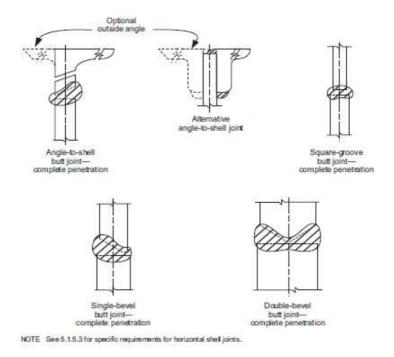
Soldaduras para juntas horizontales, F5.2 API 650.
